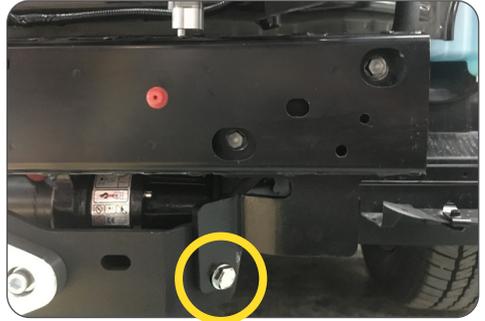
Befestigung Versteifung mit Windenplatte rechts / mounting stiffener, right side
